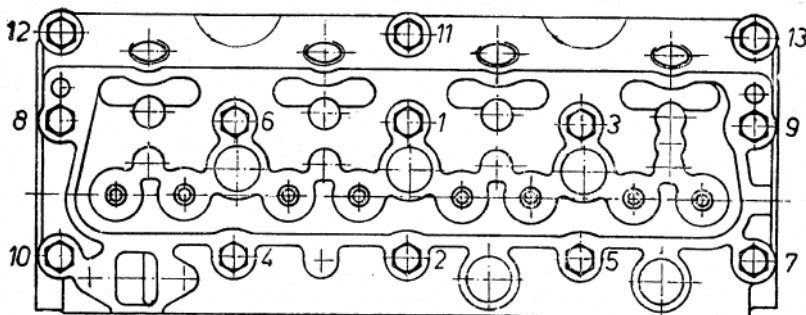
Reihenfolge für das Anziehen der Zylinderkopfbefestigungsschrauben in 3 Stufen
